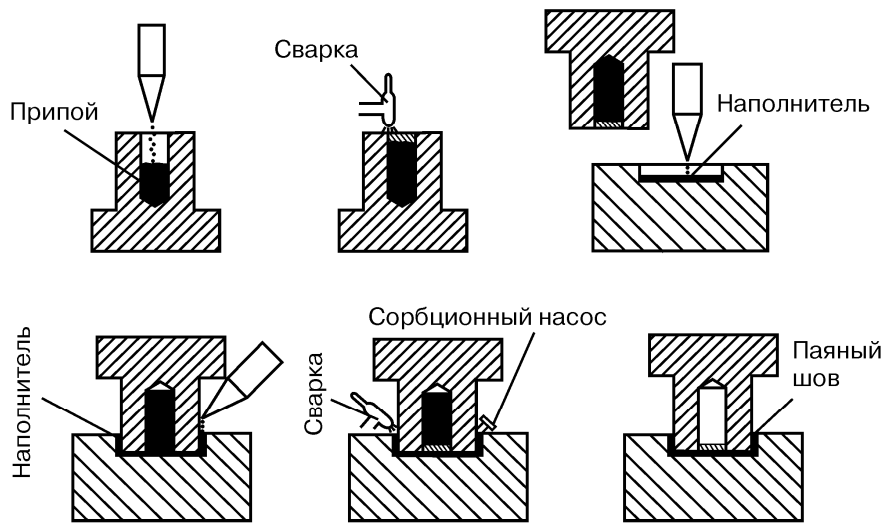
Схема зборки деталей при широкому зазорі для автовакуумного паяння
